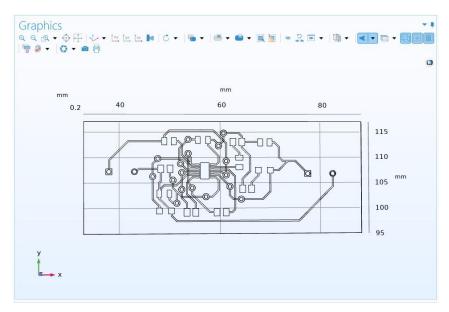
'da baskı devrenin sinyal yollarının malzemesi bakır olarak tanımlanmıştır. PCB ölçüleri 55mmx22mm olarak belirlenmiştir.
